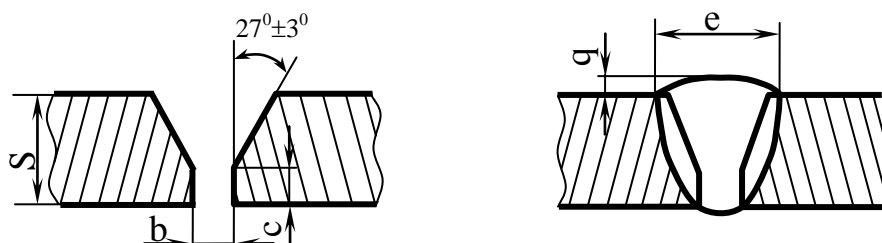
Сварное соединение до и после сварки
